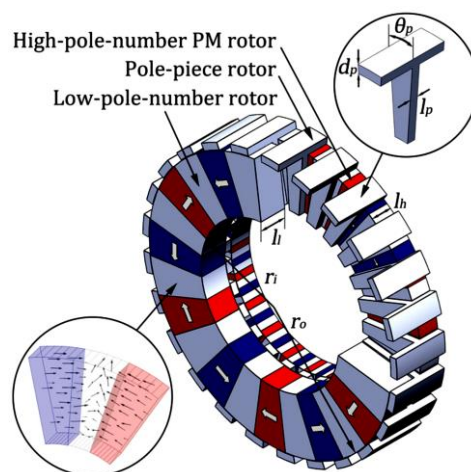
Engrenage magnétique à flux hybride à pièces ferromagnétiques en forme de T [YIN15].
